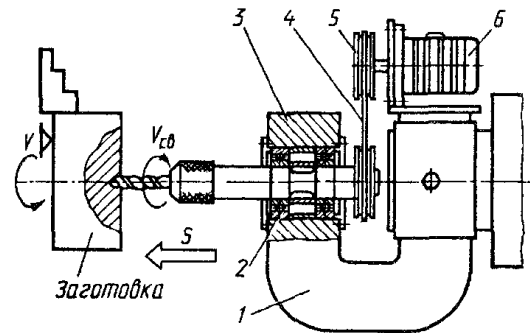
Пристрій до токарного верстата для свердління отвору малого діаметра: 1 – серга; 2 – підшипник; 3 – шпиндель; 4 - пасова передача; 5 – косинець; 6 – електродвигун
